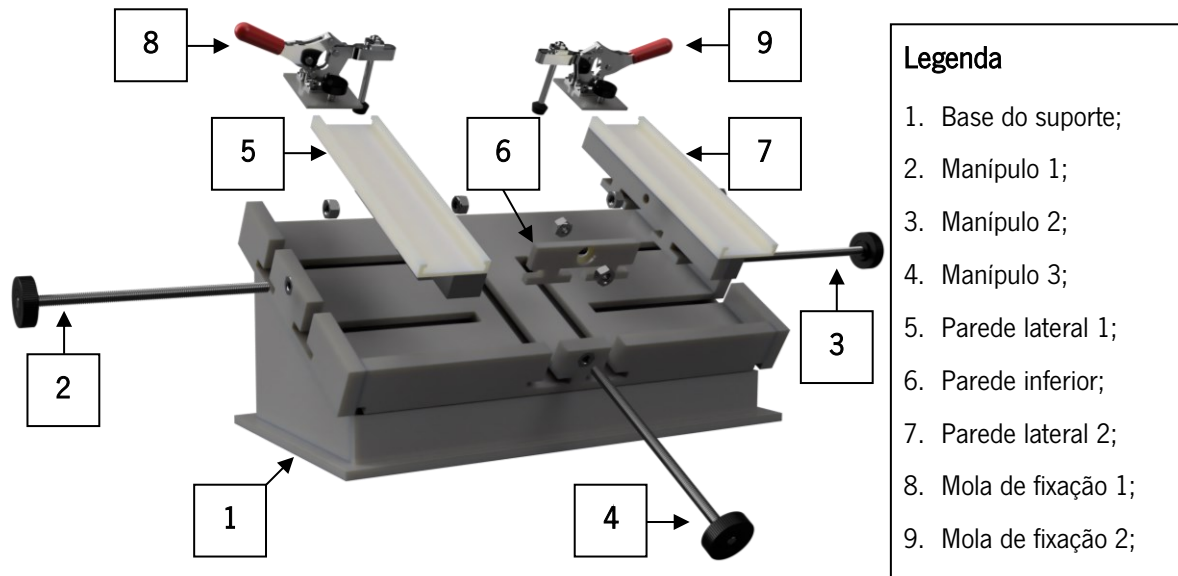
Vista explodida e legenda do suporte ajustável desenvolvido.
